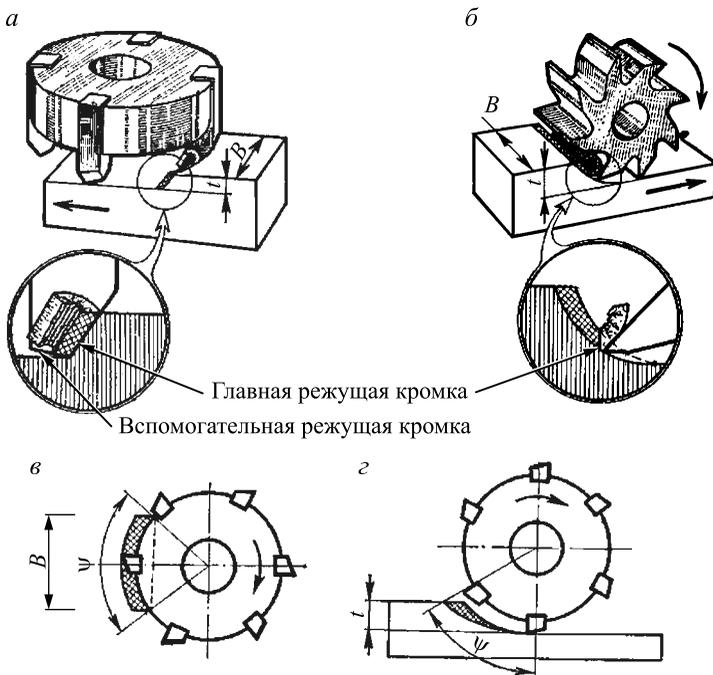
Фрезерование торцовой фрезой (а, в) и цилиндрической (б, г)
